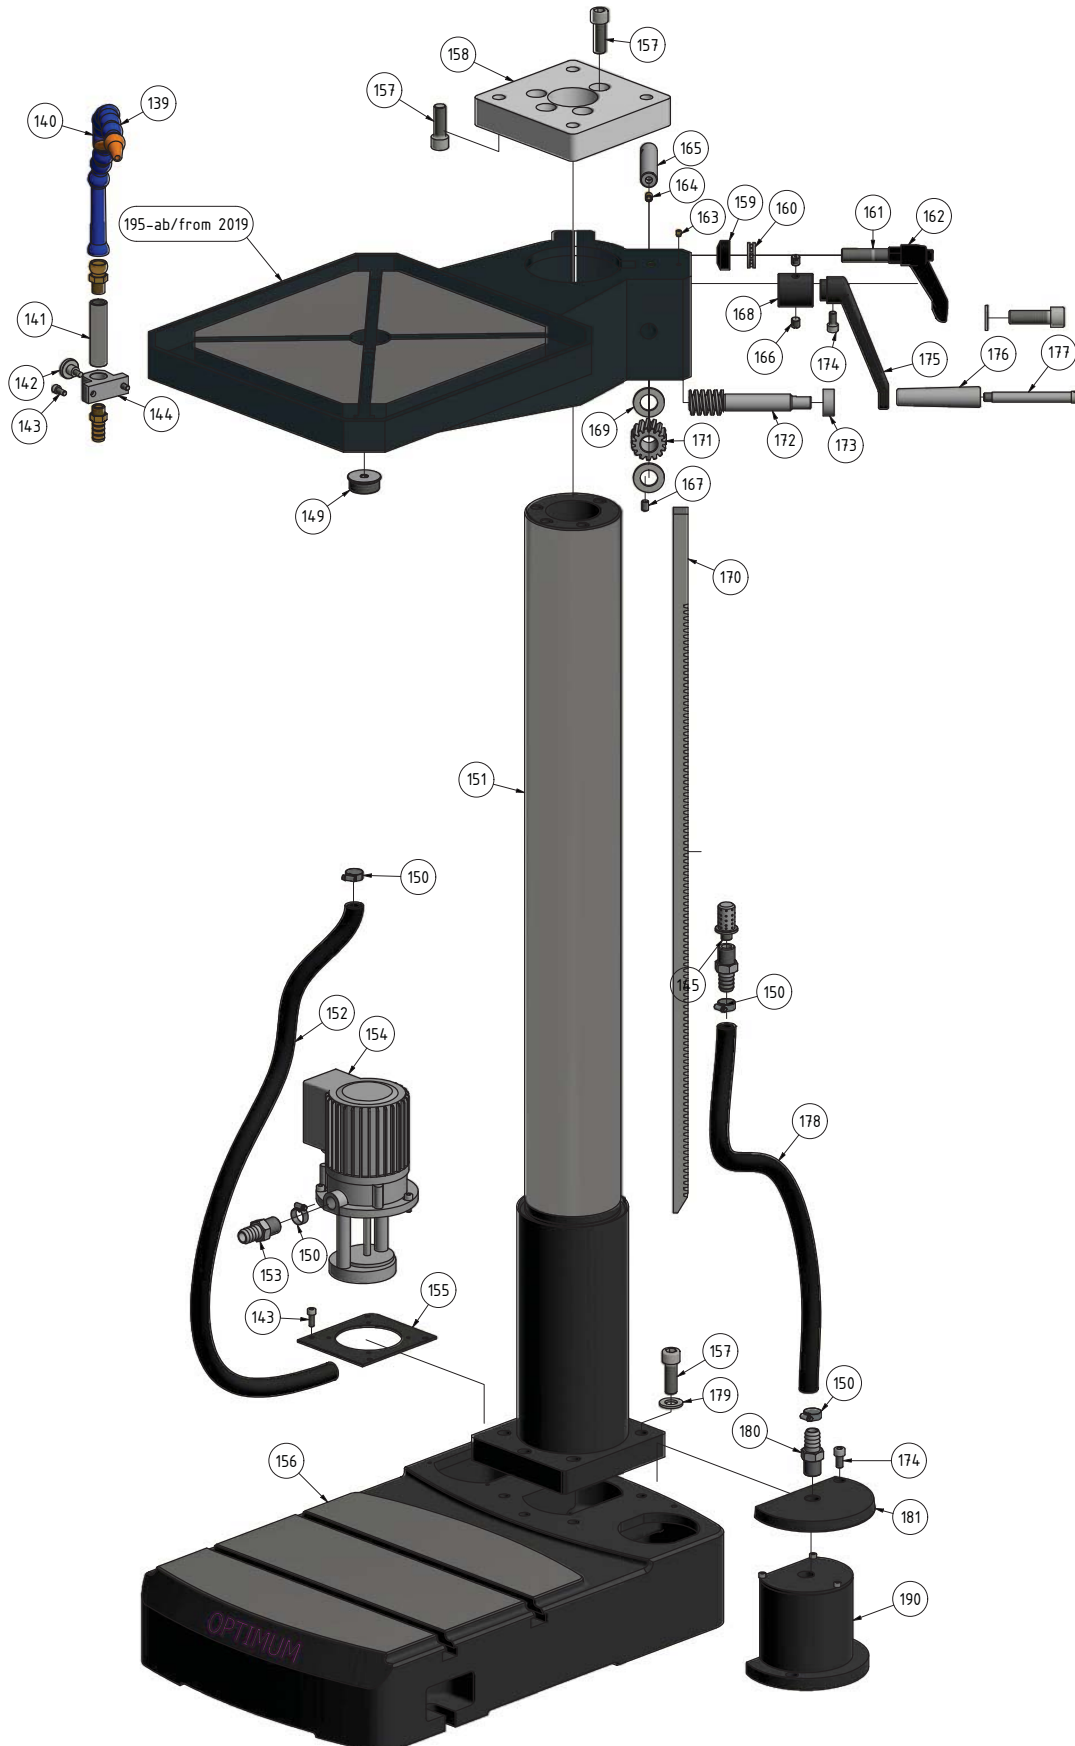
Säule und Bohrtisch - Column and drilling table
